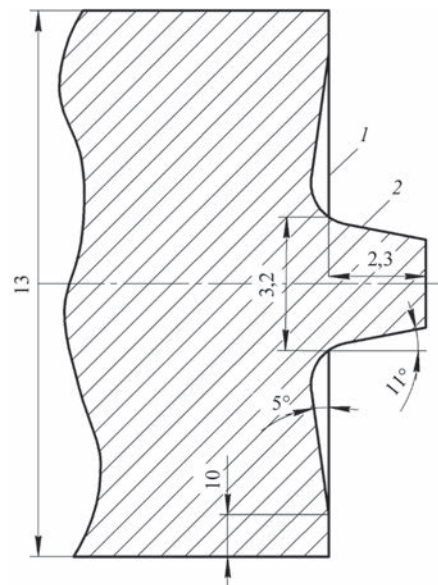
Схематичне зображення робочого інструмента для ЗТП: 1 — заплечик; 2 — штир
